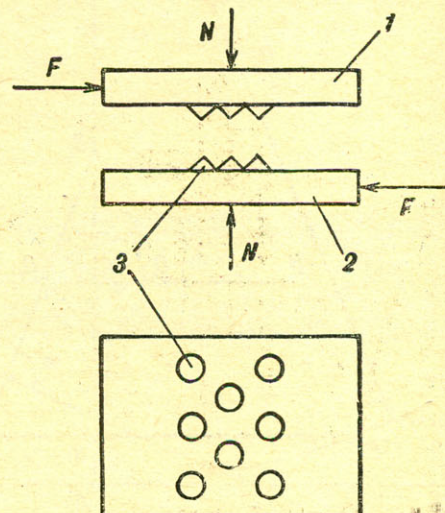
Схема сварки сдвигом: 1—2 — свариваемые детали, 3 — выступы, N — сдавливание (нагрузка), F — усилие сдвига.
